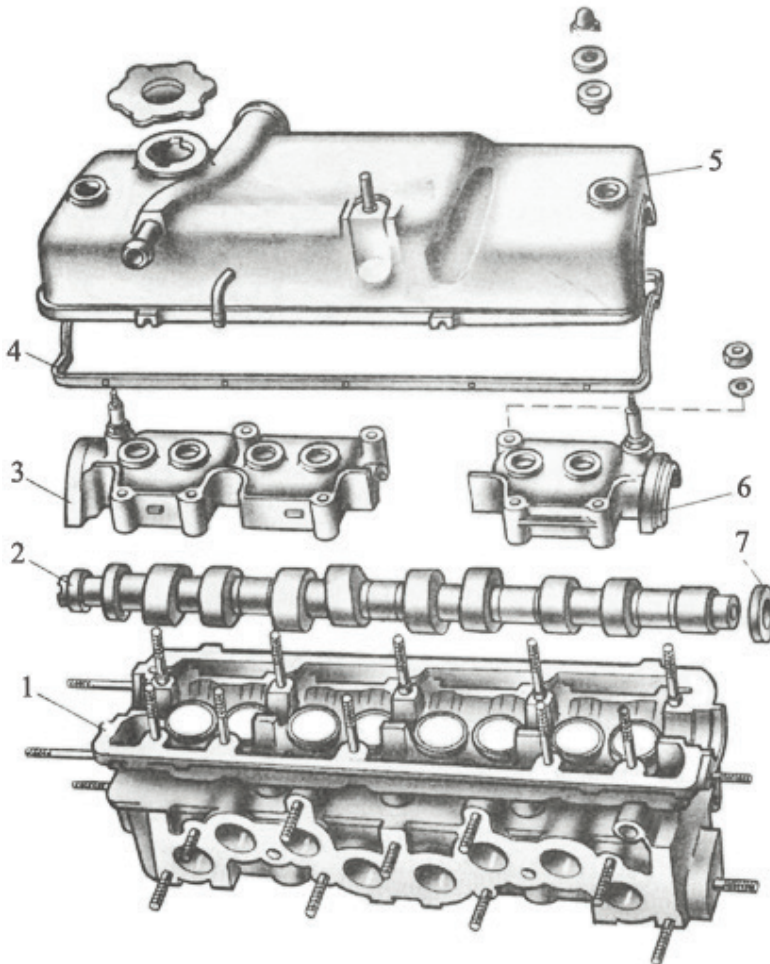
Головка цилиндров двигателя ВАЗ-2108:
